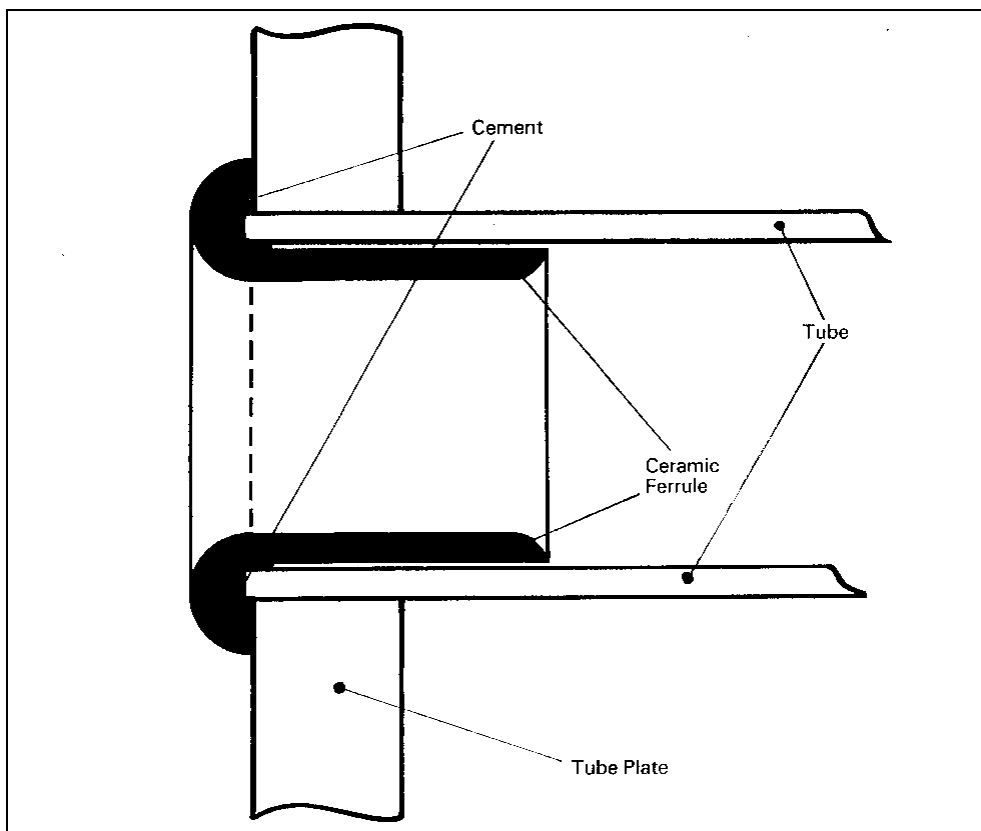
Detalle instalación protección cerámica en unión tubo a placa.
